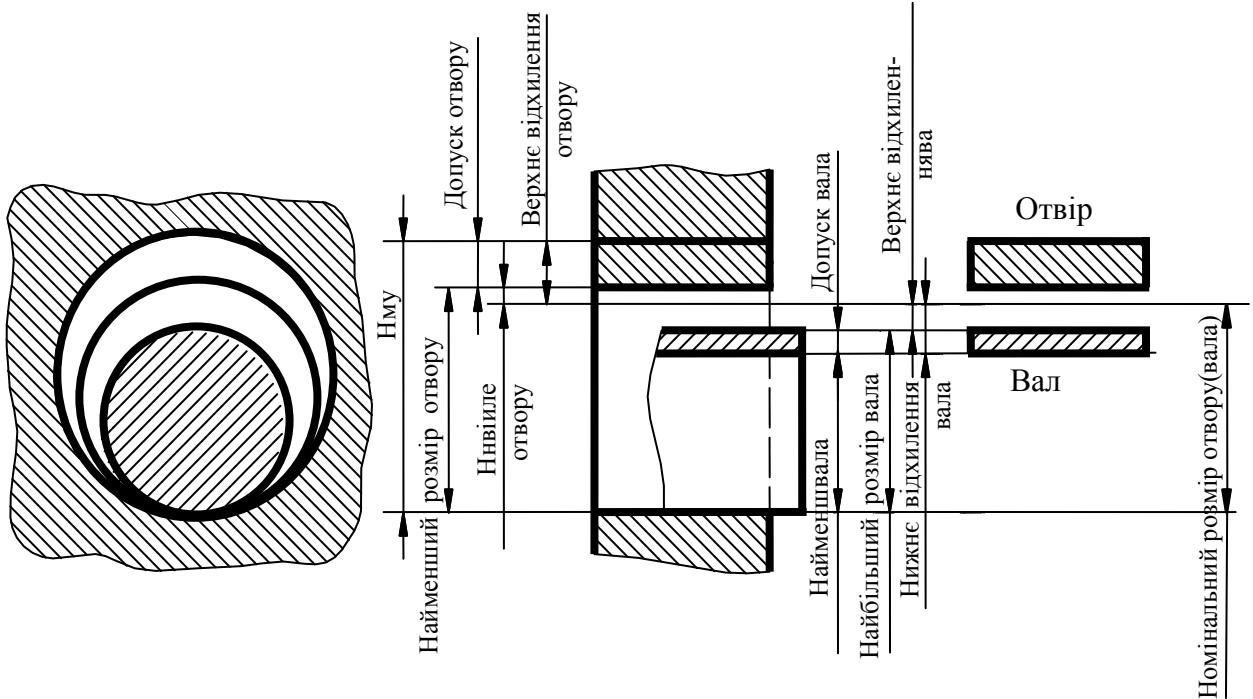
Поля допусків отвору і вала в з'єднанні із зазором (відхилення отвору додатні, відхилення вала від'ємні)
